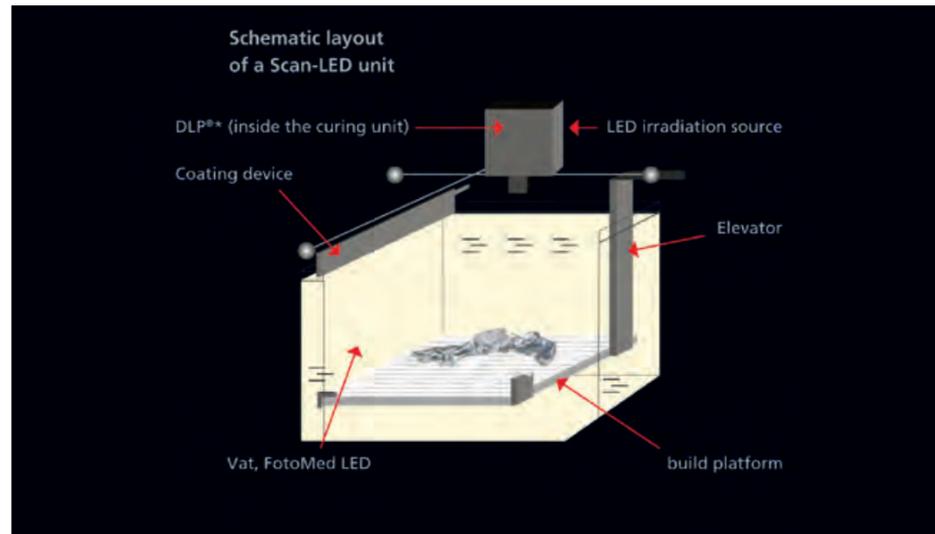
Der Aufbau einer Scan-LED Maschine.
